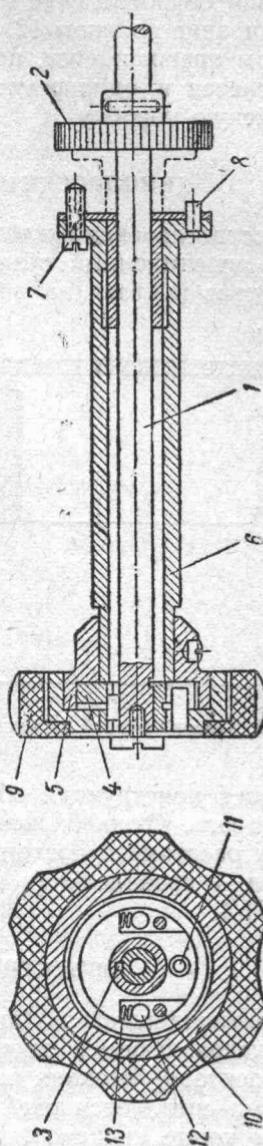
Механизм установки кадра в рамку: 1 — вал; 2 — шестерня; 3 — шпонка; 4 — поводок; 5 — втулка; 6 — кронштейн; 7 — винт; 8 — штифт; 9 — рукоятка; 10, 11 — пальцы; 12 — ролики; 13 — пружина
